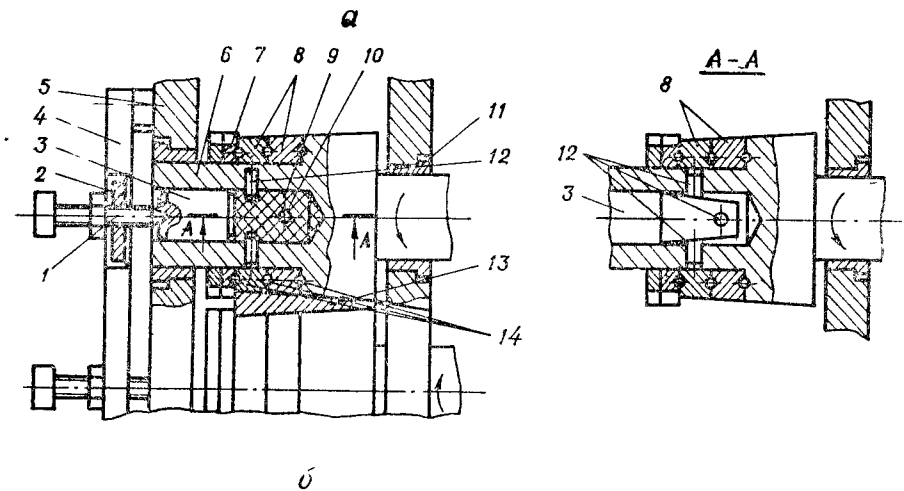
Схемы валков для прокатки винтовых лент (а) и схема валков с регулировкой значения усилия захвата (б).
